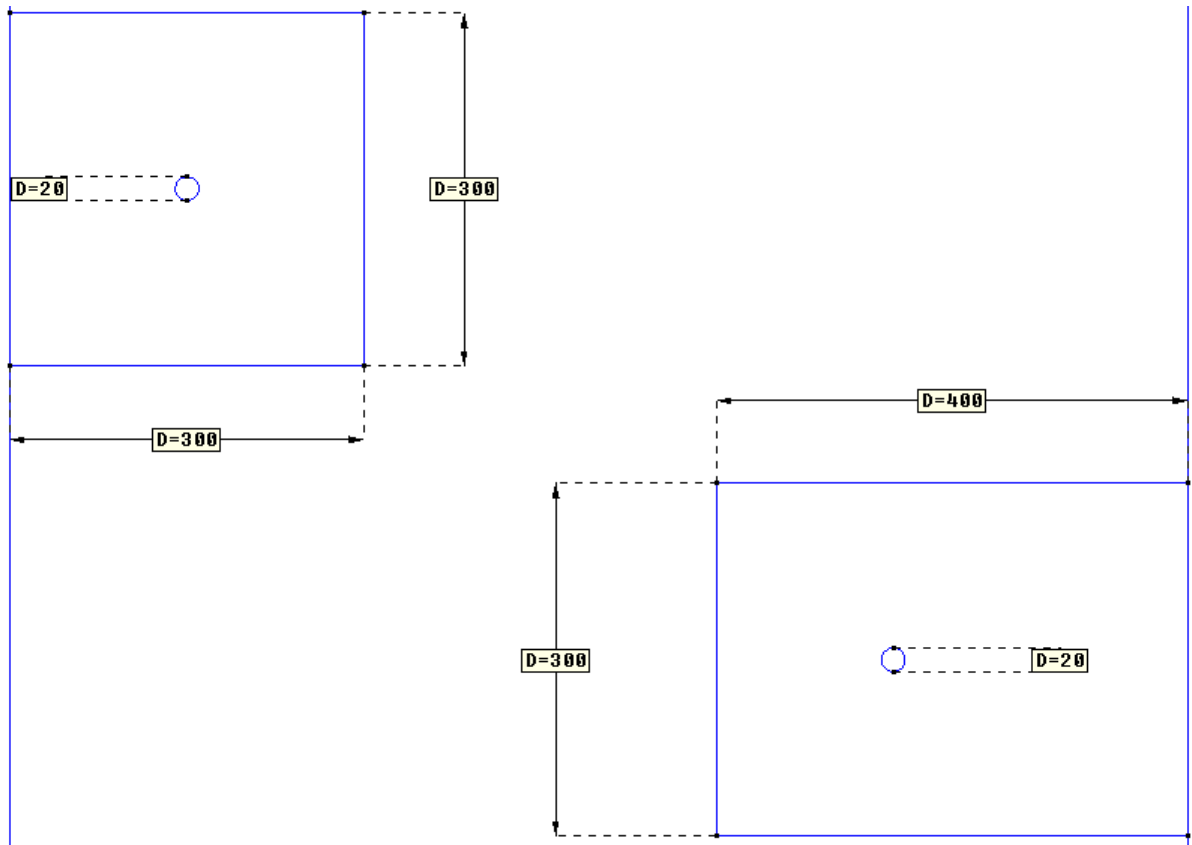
Vista en detalle (pozos) de las cotas en el Plano XY
